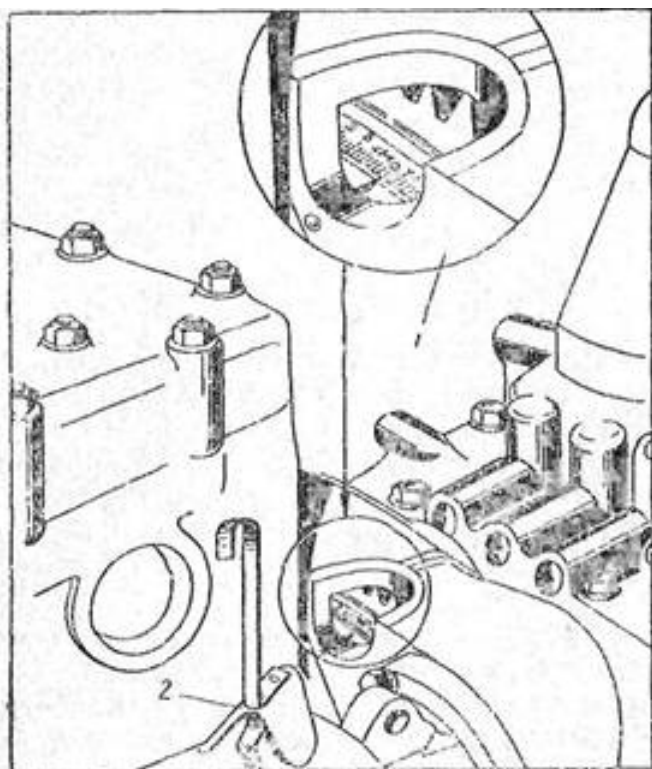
Установка верхней мертвой точки поршня первого цилиндра:
